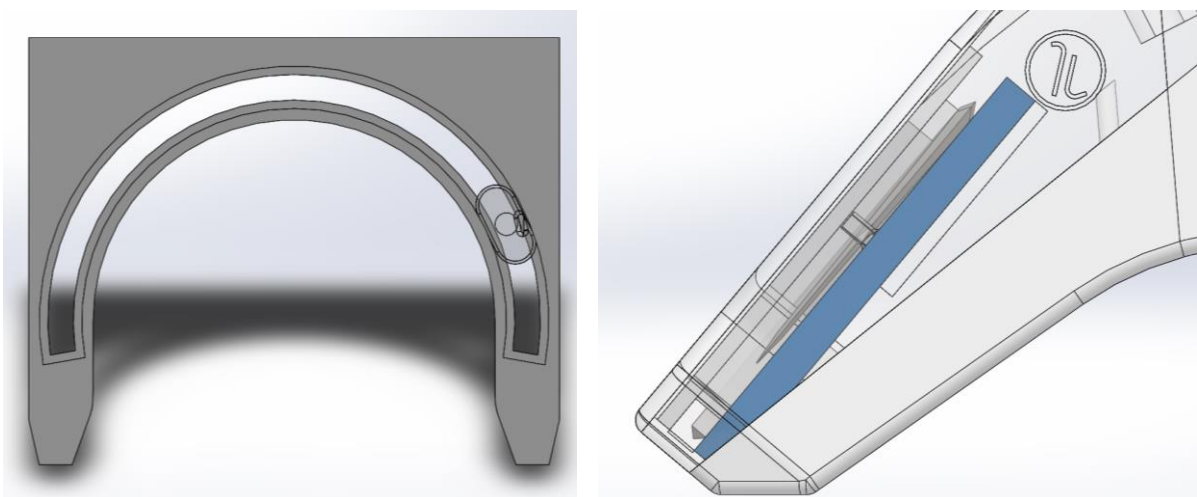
Vista en planta de la guía del carrito (izq) y su colocación en el dispositivo (dcha)
